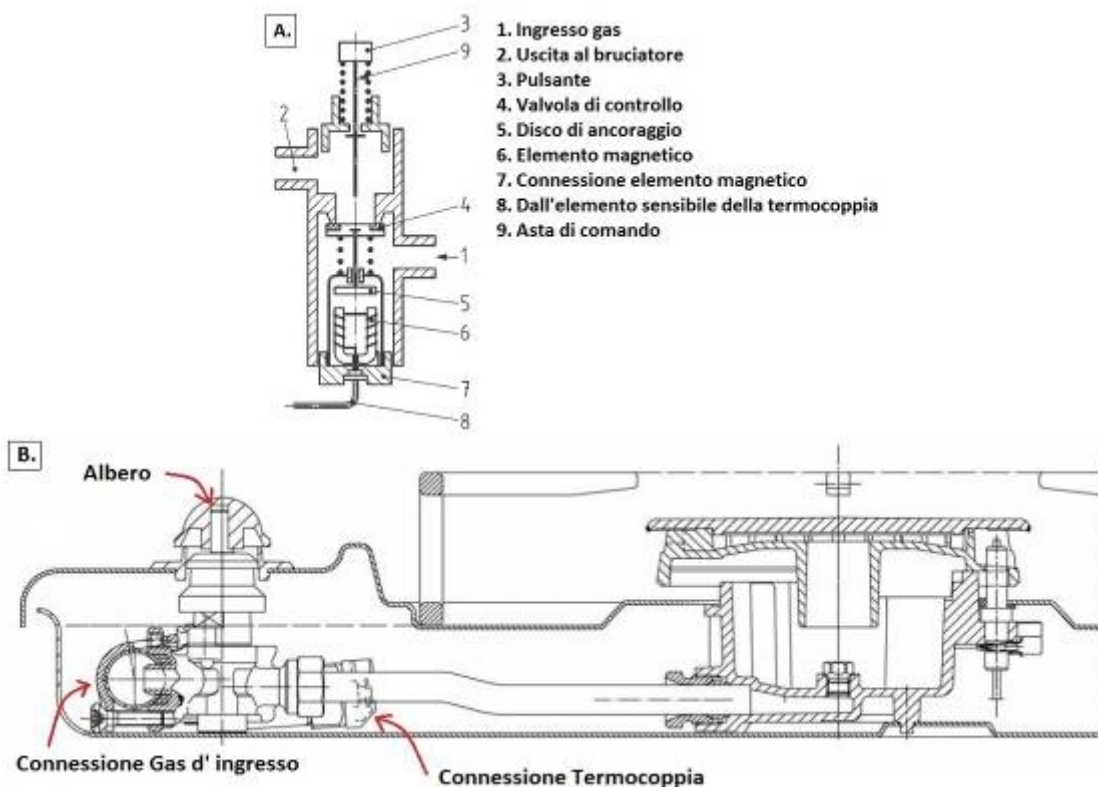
A. Componenti di rubinetto con sicurezza termoelettrica. B. Sezione di piano cottura con connessione tra rubinetto e bruciatore .
